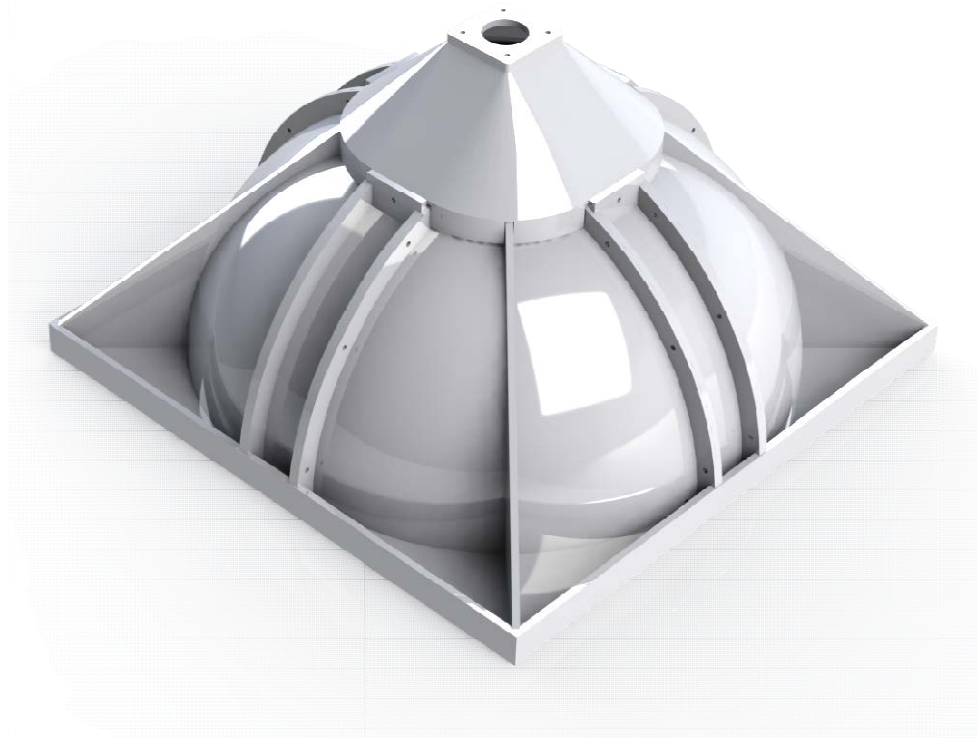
Ensamblaje del domo desde vista isométrica.
